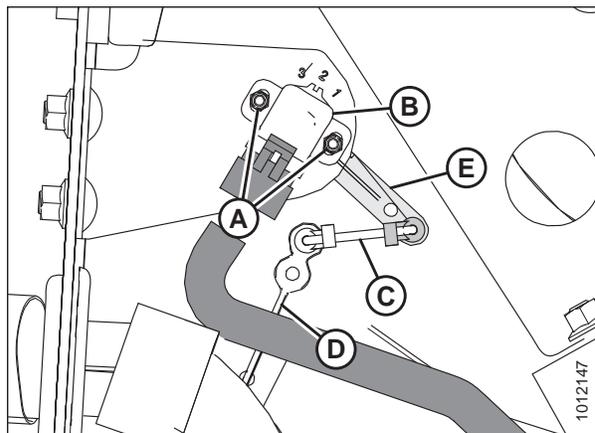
Ensamblaje del sensor de altura de la plataforma; lado izquierdo
